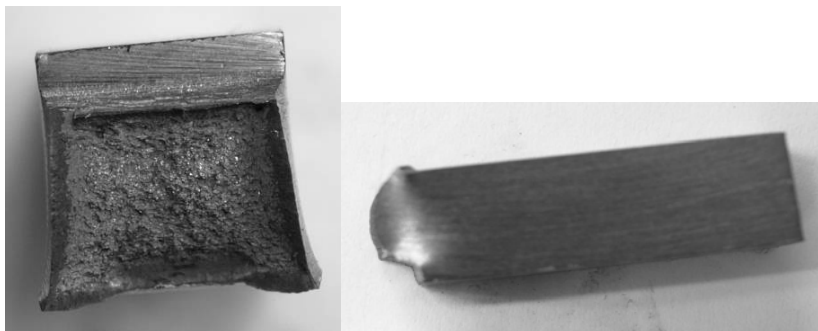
Внешний вид излома образца из деталей, подвергнутых закалке с ковочного нагрева и последующему отпуску
